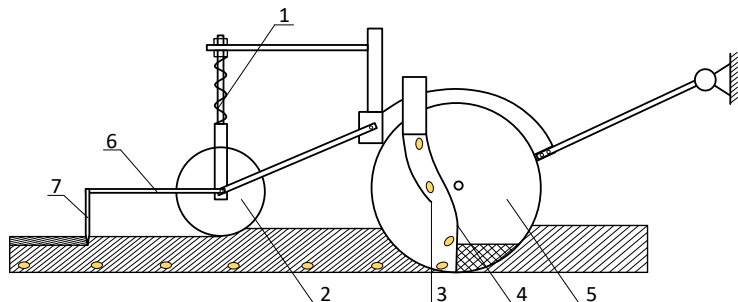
Схема и фото сошника с прикатывающим катком и рыхлителем: 1 – регулировочная пружина; 2 – прикатывающий каток; 3 – рассеиватель семян; 4 – профилеобразователь семенного ложа; 5 – сошник; 6 – тяга рыхлителя; 7 – зубья рыхлителя
